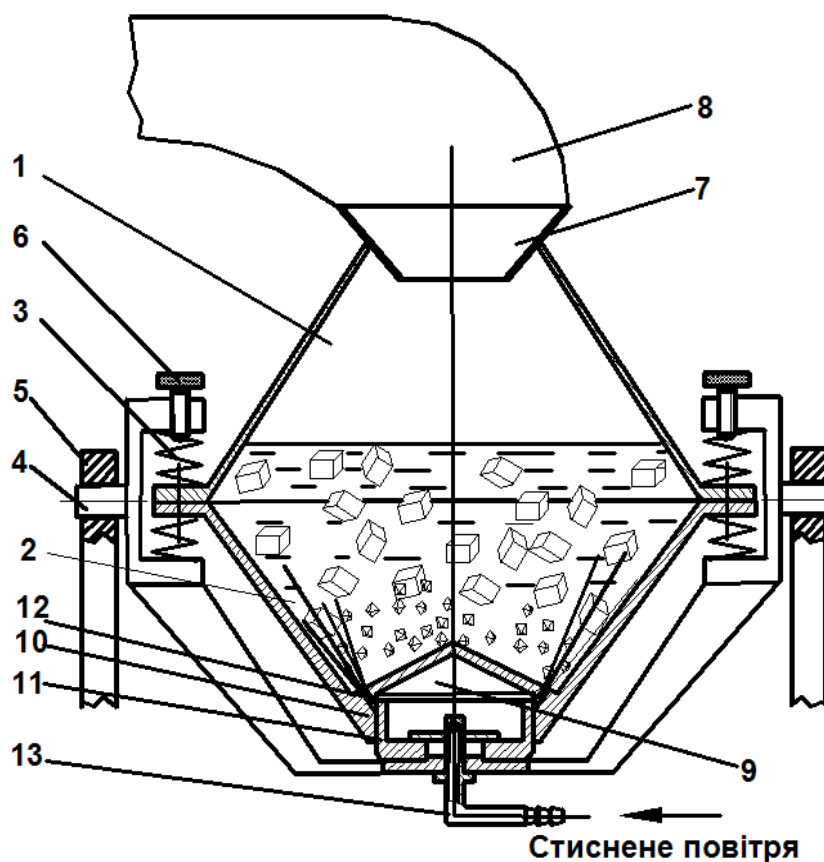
Установка для абразивної обробки дрібних деталей затопленими струменями
